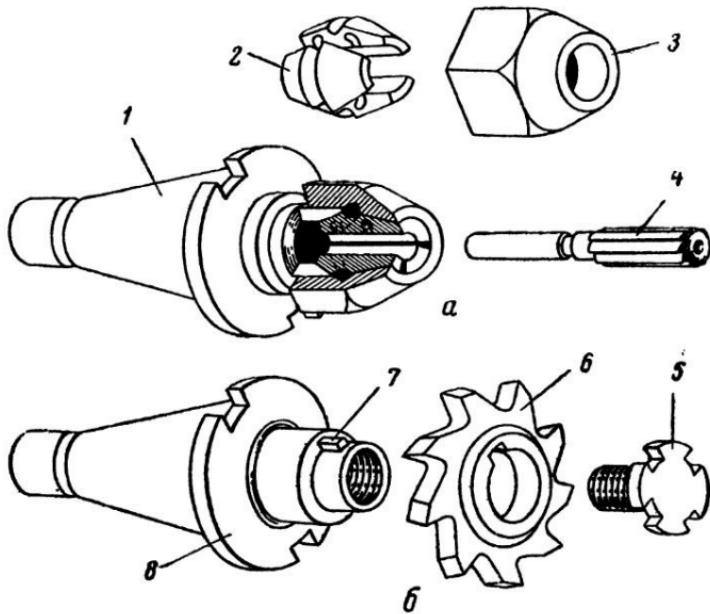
Приспособления для консольного крепления фрез: а — цанговый патрон для крепления пальцевых фрез (1 — шпиндельная оправка, 2 — цанга, 3 — патрон, 4 — фреза); б — шпиндельная оправка для крепления дисковых фрез (5 — крепежный болт, 6 — фреза, 7 — шпонка, 8 — оправка).
